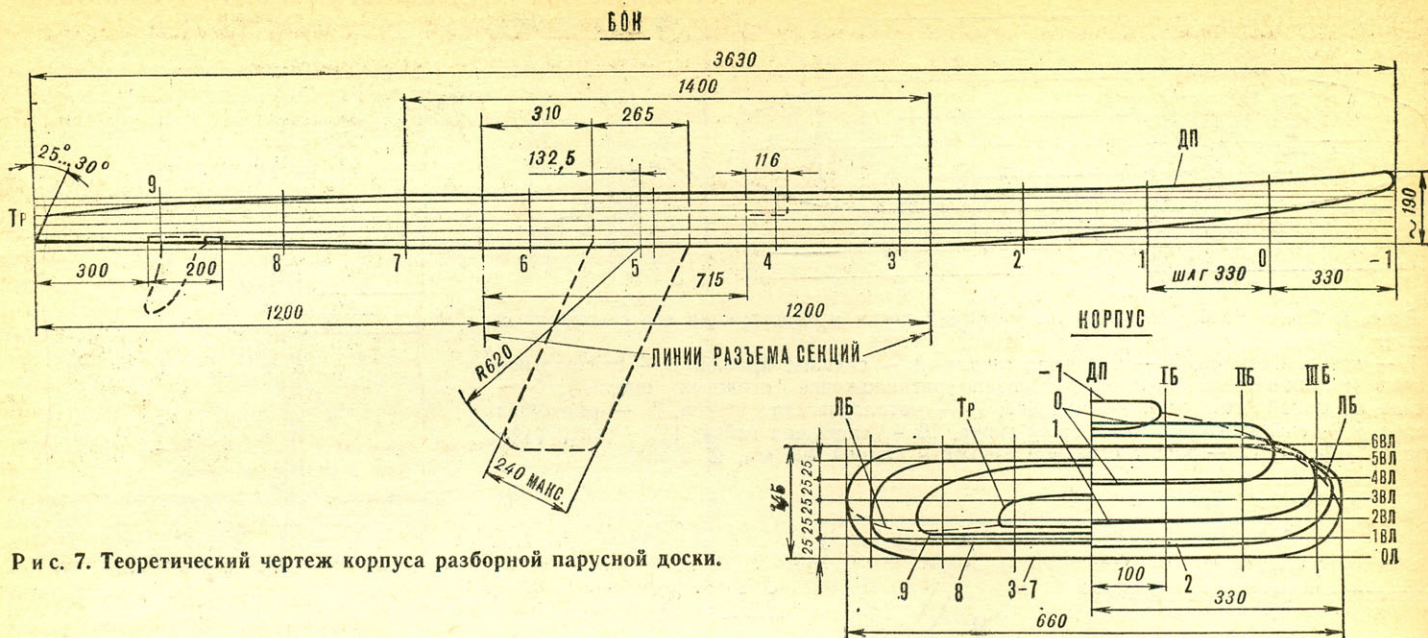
Теоретический чертеж корпуса разборной парусной доски.
